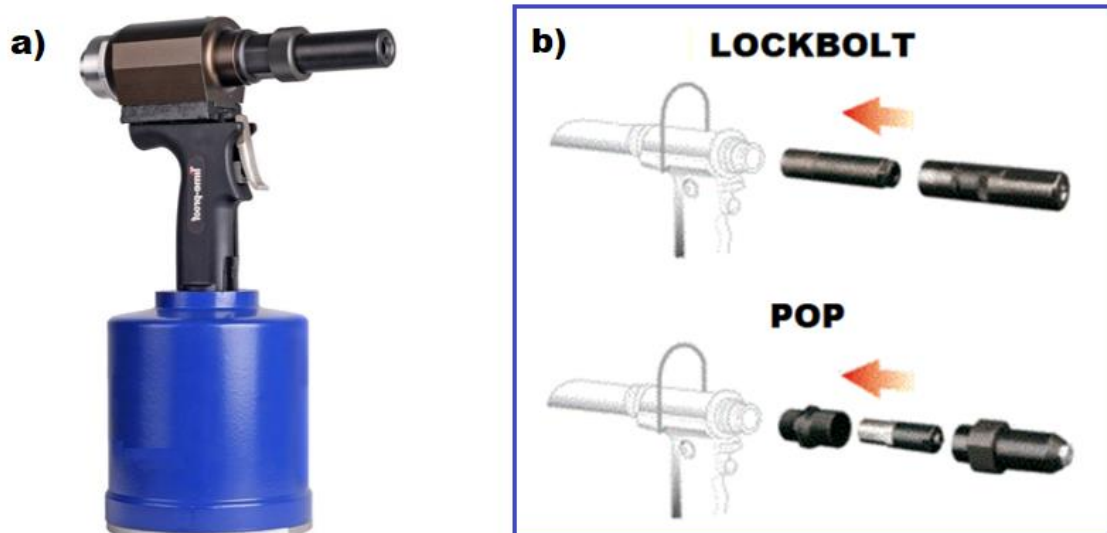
Mecanismo de pistola de rebiteagem: a) Pistola Lockbolt; b) Comparação da estrutura fundamental das pistolas Lockbolt e POP [Adaptado de (Alibaba.com) e (Tools M. A., 2018)].
